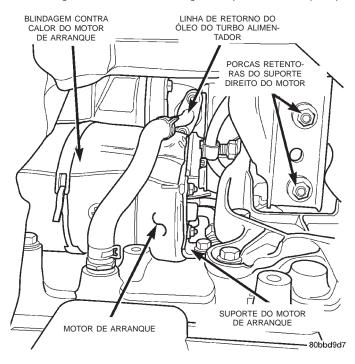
Porcas Retentoras do Suporte Direito do Motor
